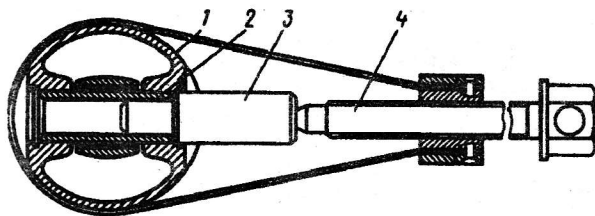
Выпрессовка поршневого пальца из поршня съемником 7823-6102:
